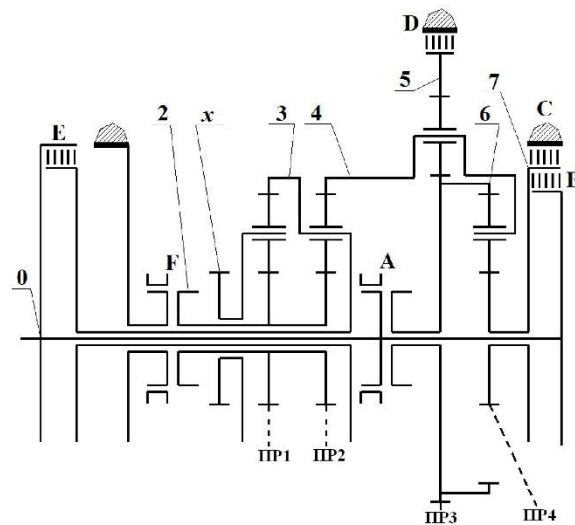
Кінематична схема коробки передач ZF 9HP
